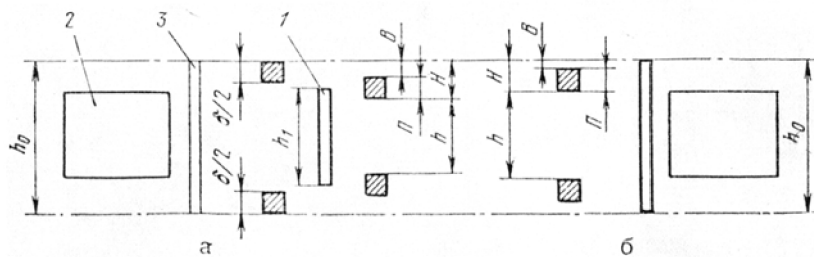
Схема полей допусков при системе вала (а) и широкоходовой посадке (б): h_0 - расчетный размер, h_1 - минимальный размер, h - номинал с полем допуска $\Pi=H-V$
